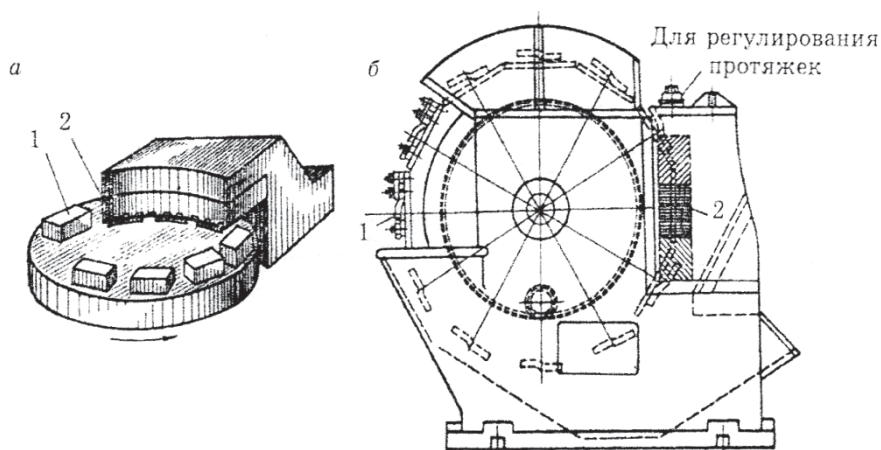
Схемы работы станков для непрерывного протягивания:
